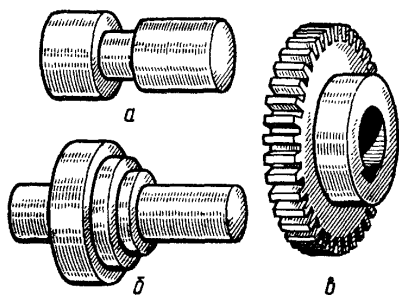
Типові деталі, що виготовляються на токарних верстатах:
